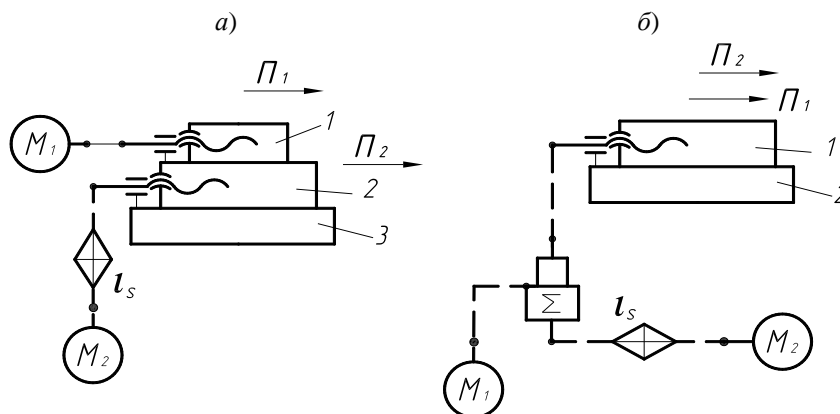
Варианты компоновки исполнительного устройства для осуществления двух движений двумя подвижными блоками (а) или одним подвижным блоком (б)
